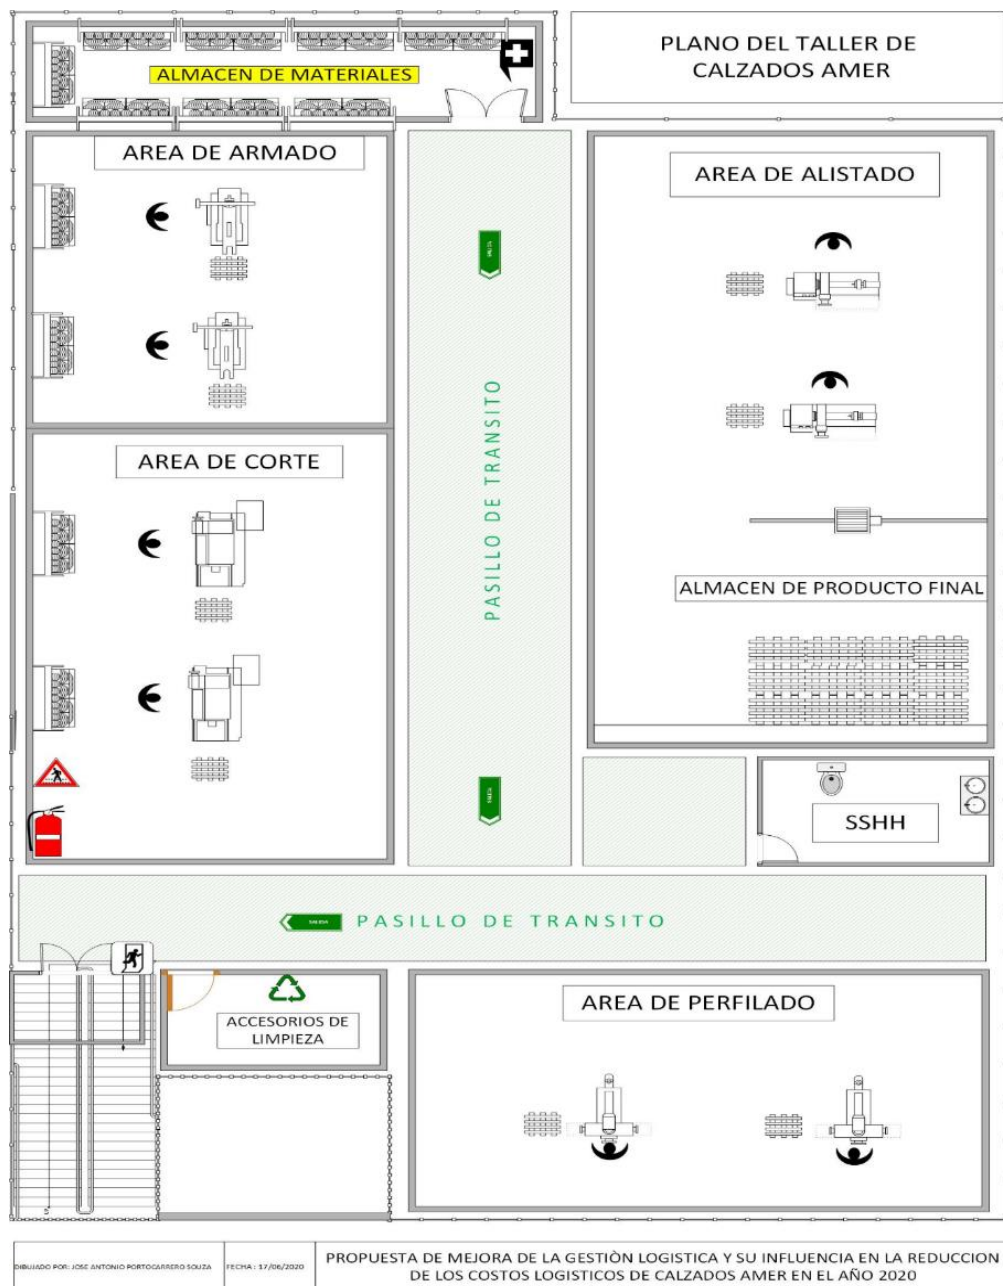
Layout de Calzados Amer. Fuente: Elaboración Propia
